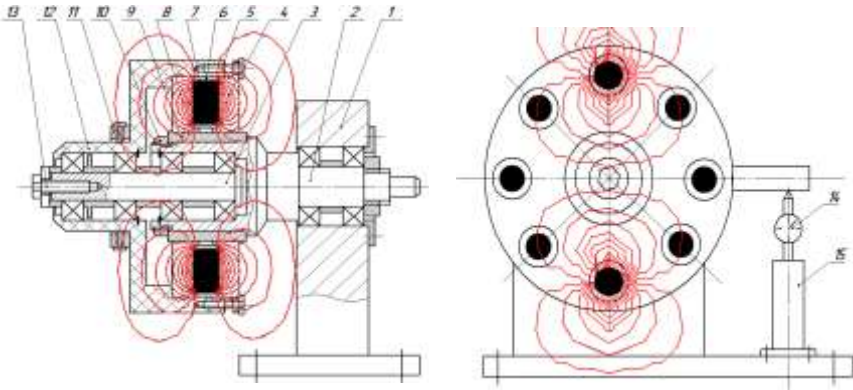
Схема экспериментальной установки: 1 – стойка; 2 – подвижный вал; 3 – неподвижный вал; 4 – съемный полюс; 5 – болт; 6 – диск; 7 – магнит; 8 – съемный полюс; 9 – сменная втулка; 10 – гайка; 11 – хомут; 12 – корпус; 13 – болт; 14 – индикатор; 15 – опора
